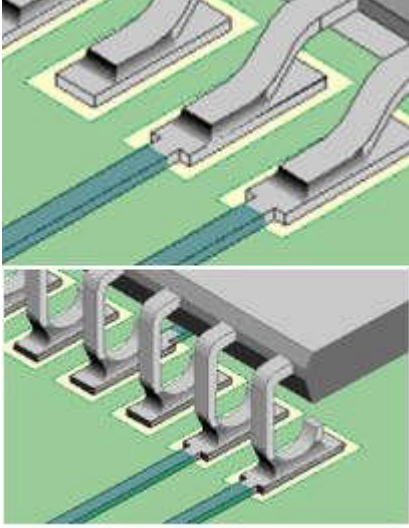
Solder-light kullanarak yüzey montaj entegrelerin sökülmesi
